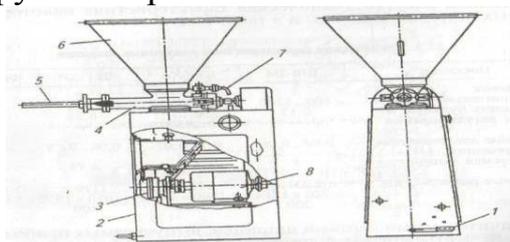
Двухцевочный вакуумный шприц ФШ2-ЛМ: 1 - педаль включения; 2 - станина; 3 - масляный шестеренный насос; 4 - корпус рабочих шнеков; 5 - цевка; 6 - бункер; 7 - вакуумная головка; 8 - электродвигатель.
